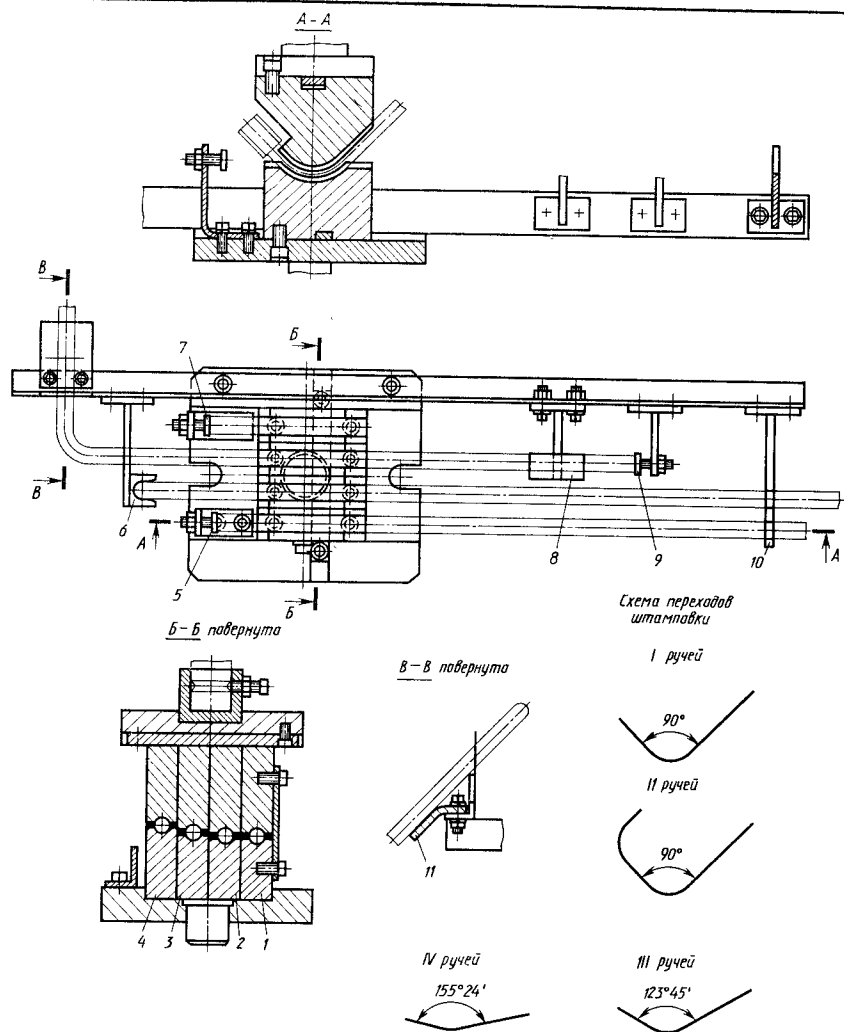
Четырехручьевый штамп для свободной гибки трубы
